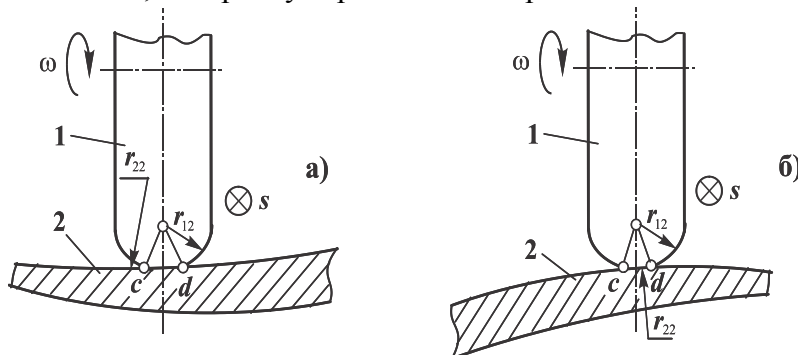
Схемы обработки поверхностей лопатки ГТД (вид спереди):
